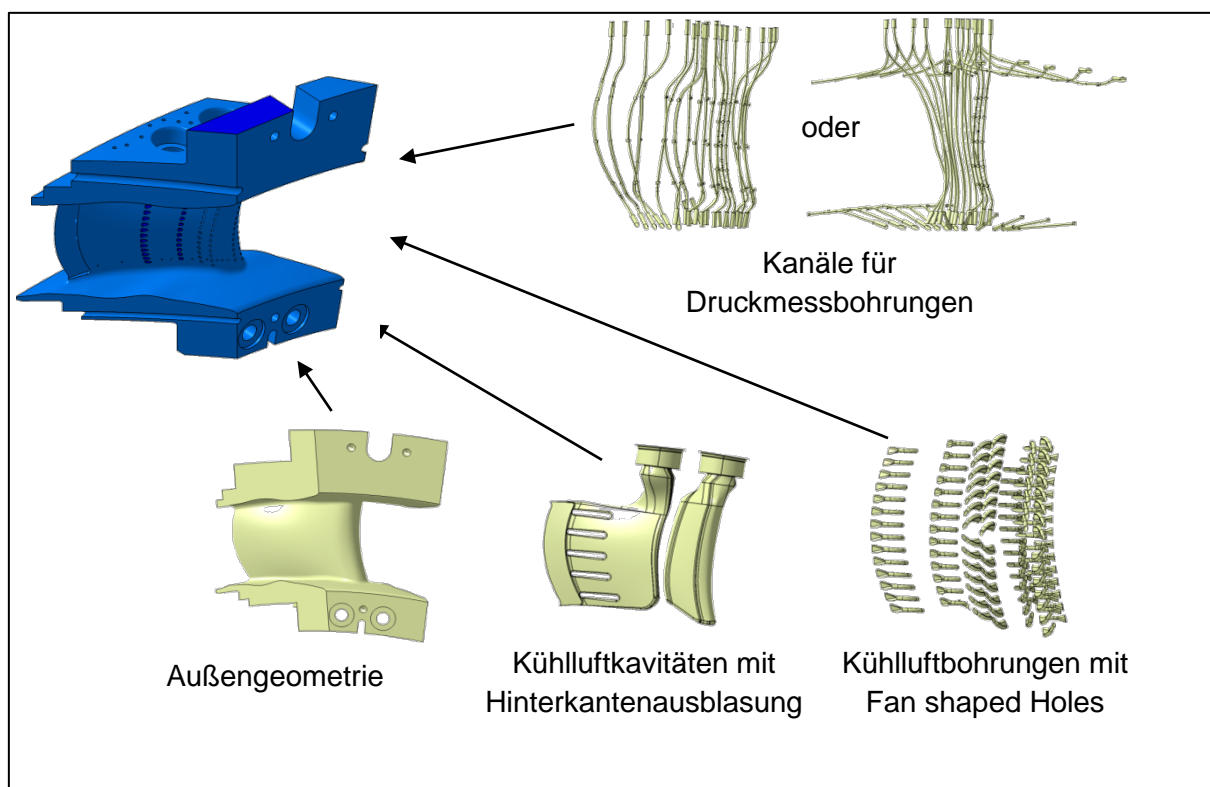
Stator-1 Schaufeln mit Kühlluftlayout und Druckmessbohrungen
